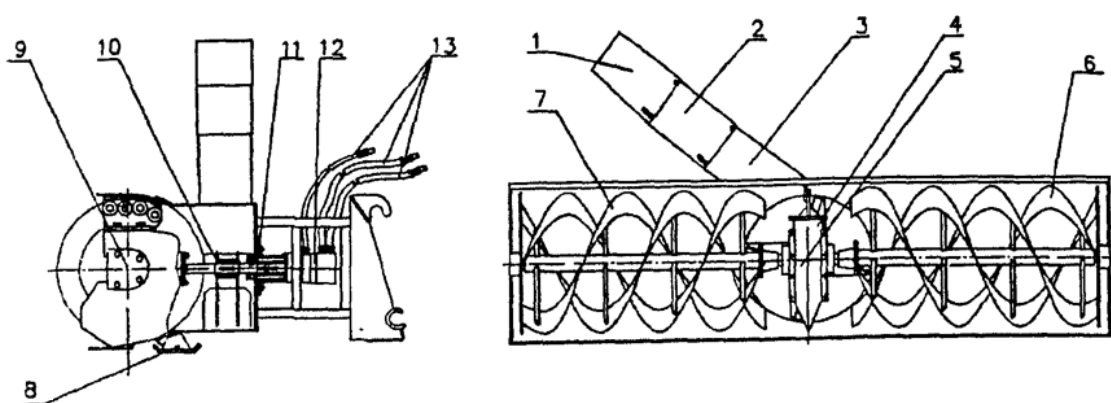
Конструктивная схема навесного фрезерно-роторного снегоочистительного оборудования
